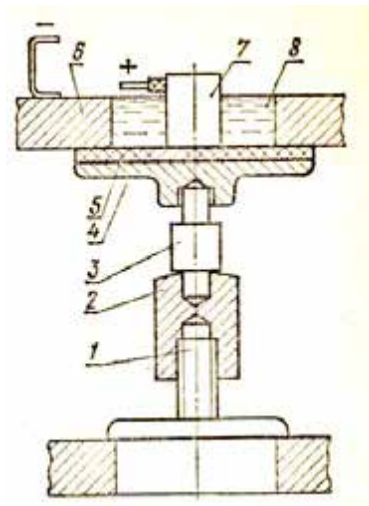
Відновлення поверхні посадочного отворів в корпусі коробки передач:
